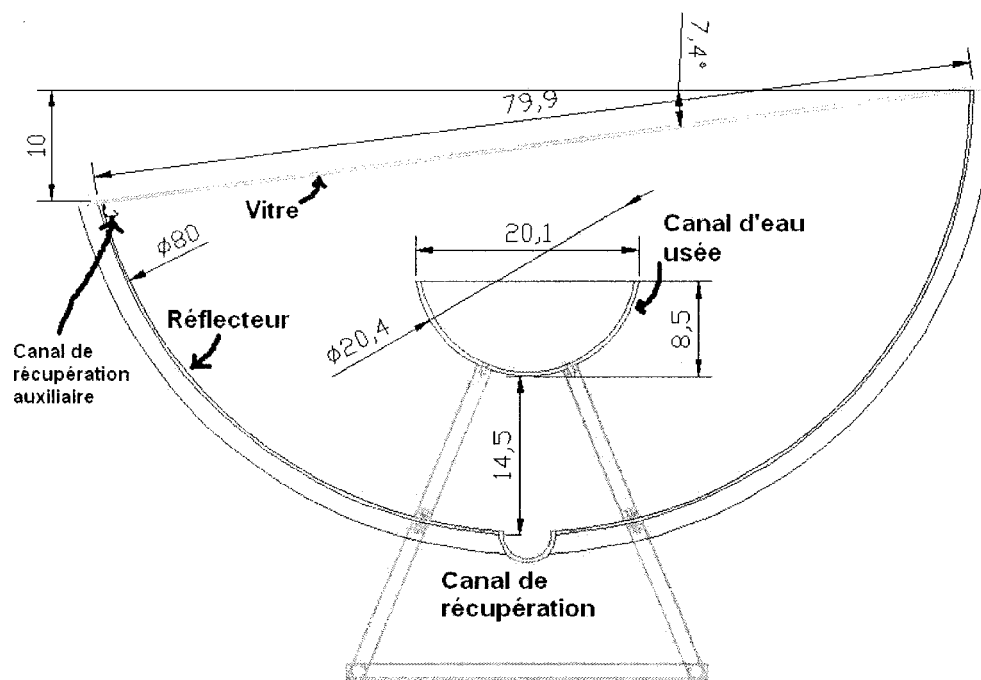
Coupe de l'appareil (dimensions en cm)
